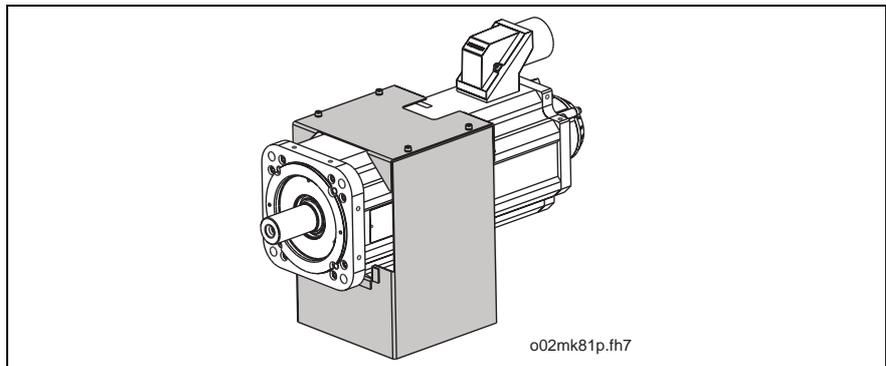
Exemplo de motor MKD com ventilação radial das superfícies
